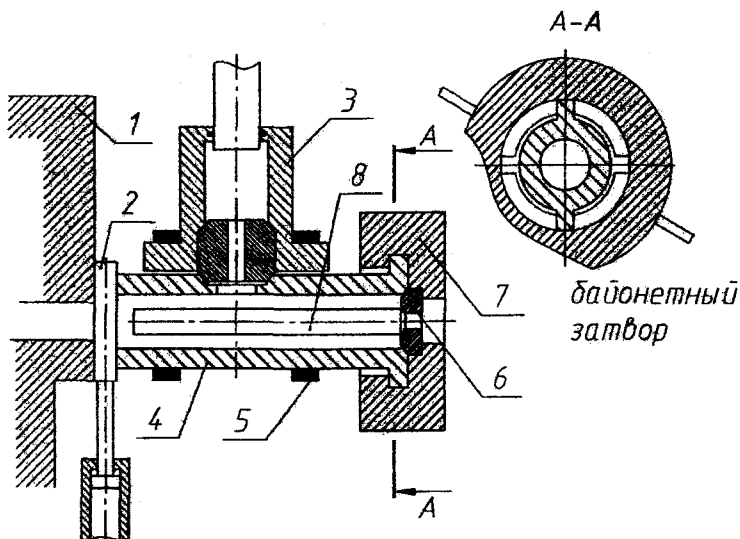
Гидростат с двумя гидроцилиндрами с приводом от ползуна пресса: 1 – станина пресса; 2 – подвижный затвор, обеспечивающий возможность загрузки заготовки через отверстие в станине; 3 – гидроцилиндр для накопления давления рабочей жидкости; 4 – главный гидроцилиндр; 5 – обмотка из металлической проволоки; 6 – матрица; 7 – крышка байонетного затвора; 8 – заготовка
